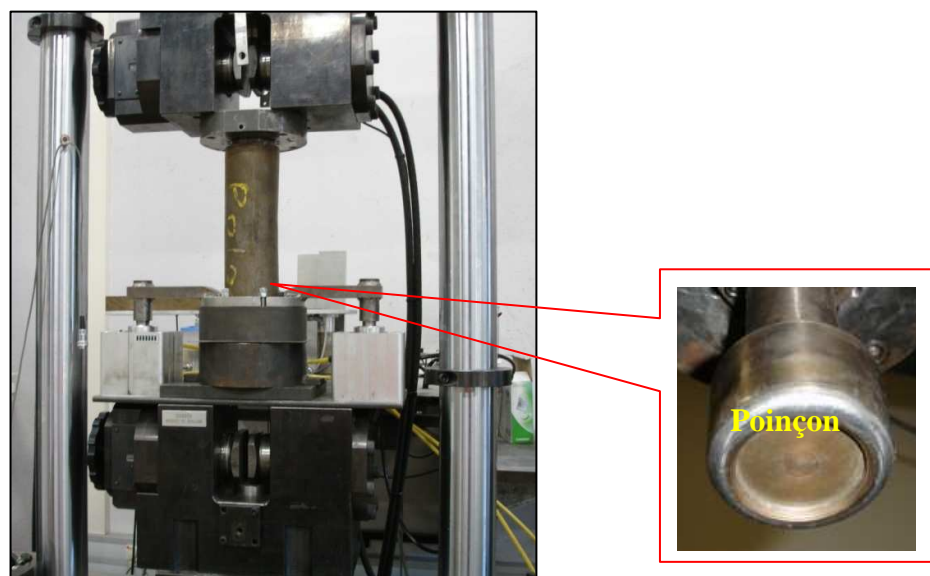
Configuration de la machine et du montage d'emboutissage de type Marciniak (CEMEF).
